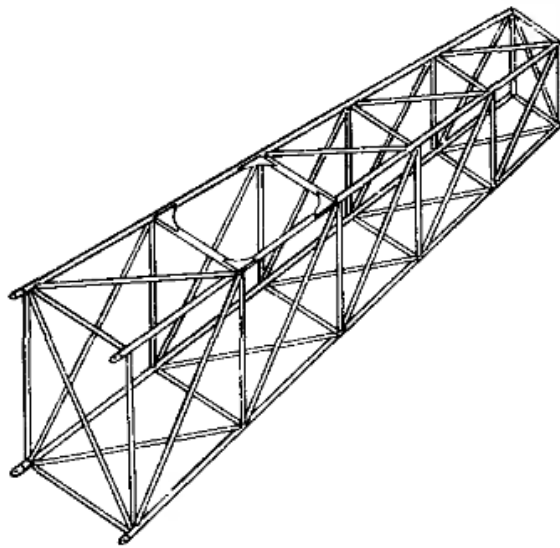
Пространственная жесткая ферма (каркас фюзеляжа)
